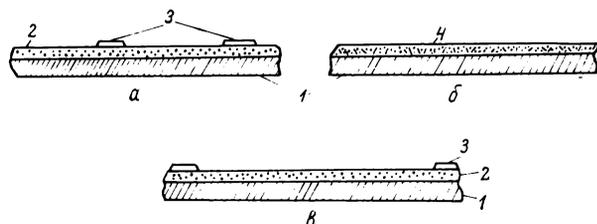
Магнитно-абразивные ленты: трехслойная лента «Зебра» — а; двухслойная абразивно-магнитная лента — б; магнитная лента с абразивными концами — в; 1 — основа; 2 — магнитный слой; 3 — абразивный слой; 4 — магнитно-абразивный слой
